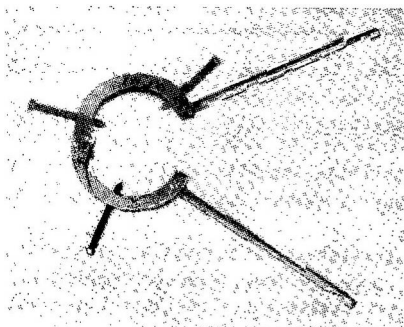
Приспособление для освобождения цанговых подъемных инструментов от ловильной шейки канатных устройств
